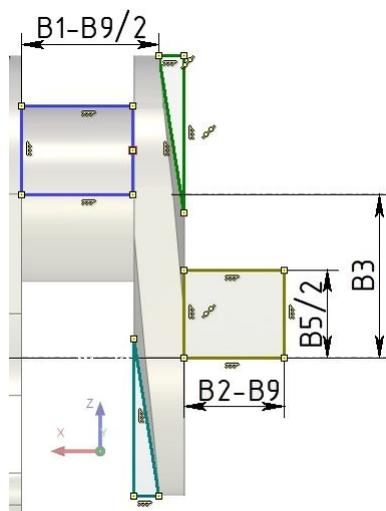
3D-профиля фаски щеки без противовеса и коренной шейки
